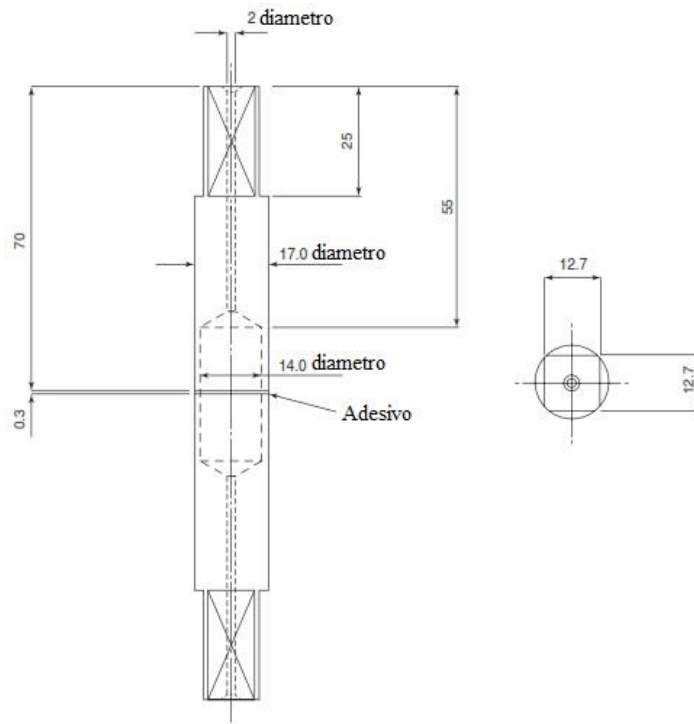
Geometria e dimensões (mm) do provete *Napkin ring* [20]
